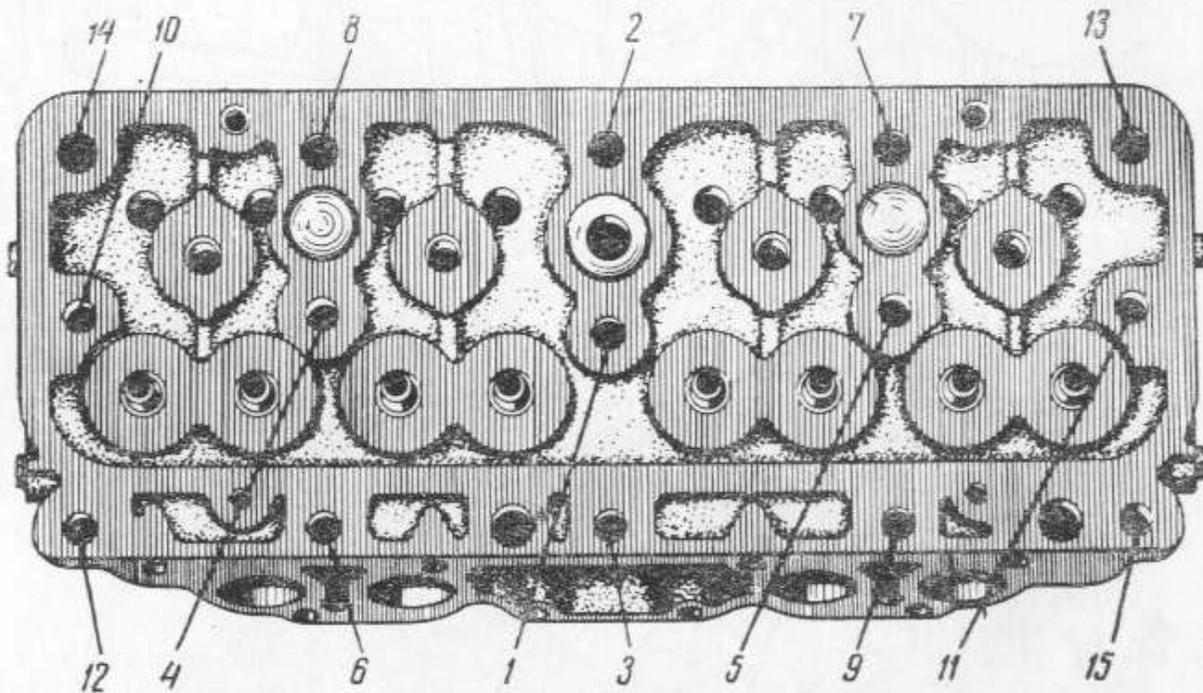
Reihenfolge des Nachziehens der Befestigungsschrauben am Zylinderkopf
